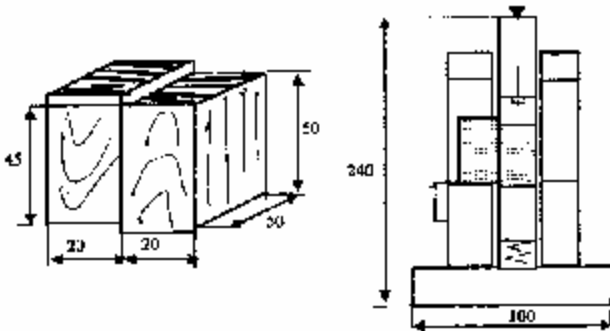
Основной образец для проверки клеящей способности клеев и приспособление для его испытания
